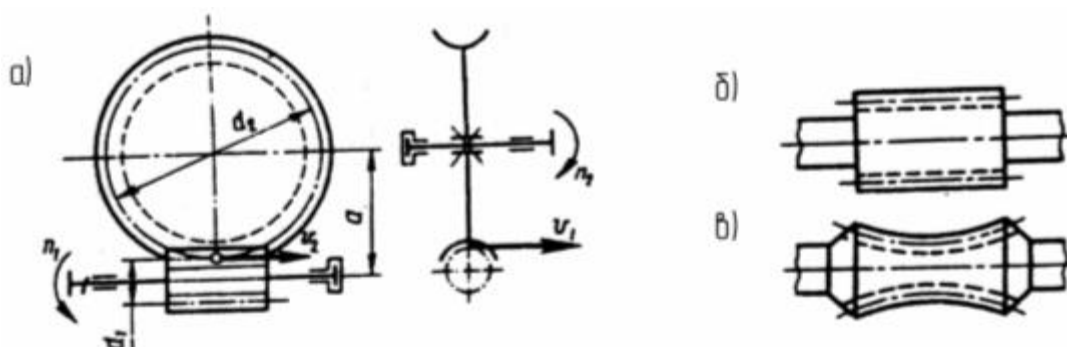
Схема червячной передачи лифтового редуктора:
